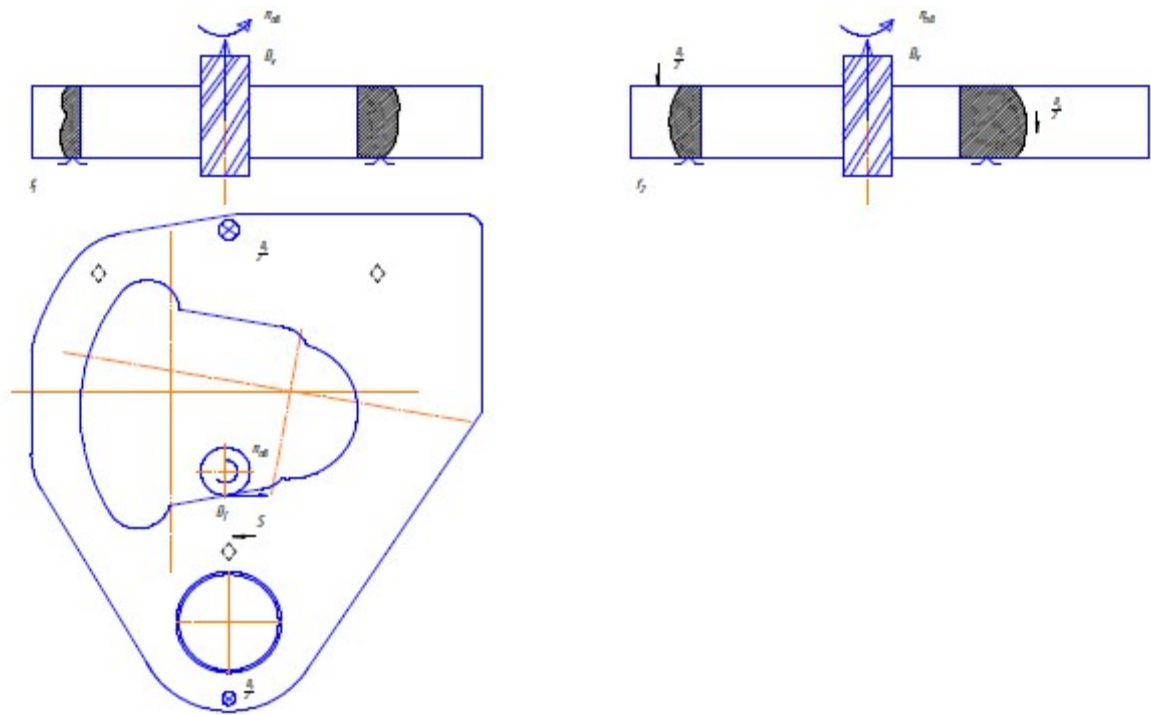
Схема сил, що діють на деталь при фрезеруванні
